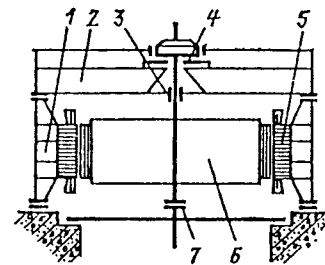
Гидрогенератор подвесного исполнения с комбинированным подпятником: 1 — корпус; 2 — верхняя крестовина; 3 — направляющий подпятник; 4 — подпятник; 5 — статор; 6 — ротор; 7 — муфта
